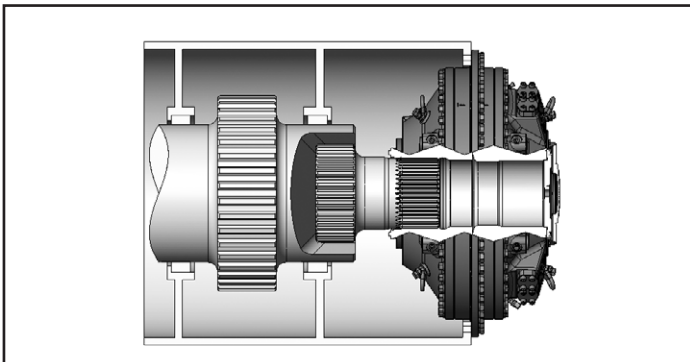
Motor mit Befestigung per Flansch und Vielkeilverzahnung sowie hoher Radialbelastung F_r an der Abtriebswelle.
